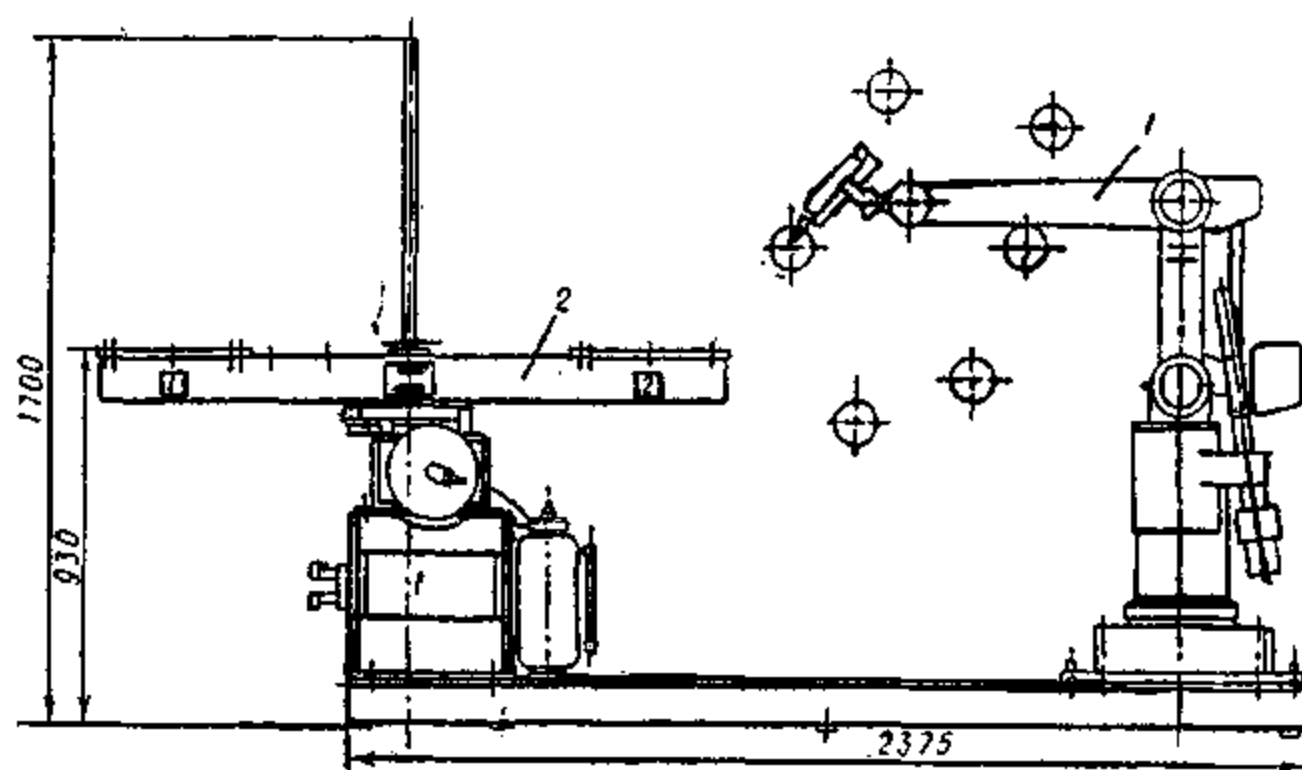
弧焊机器人ASEA与焊接变位机
